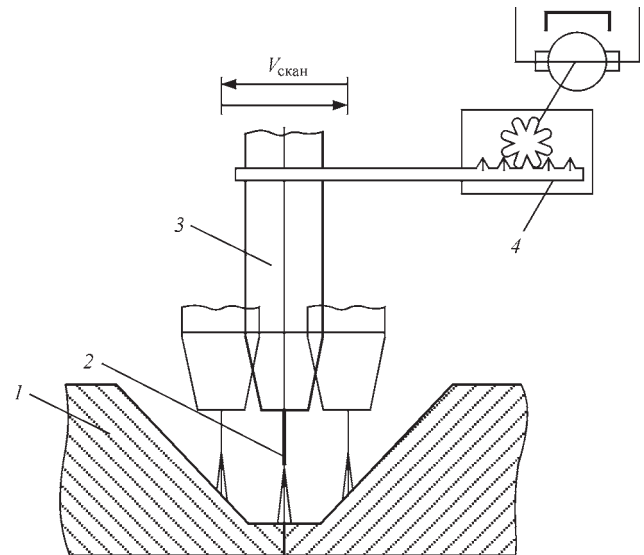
Коливальний механізм для зварювання: 1 – зварювальна деталь; 2 – електрод; 3 – пальник; 4 – механізм колювань
